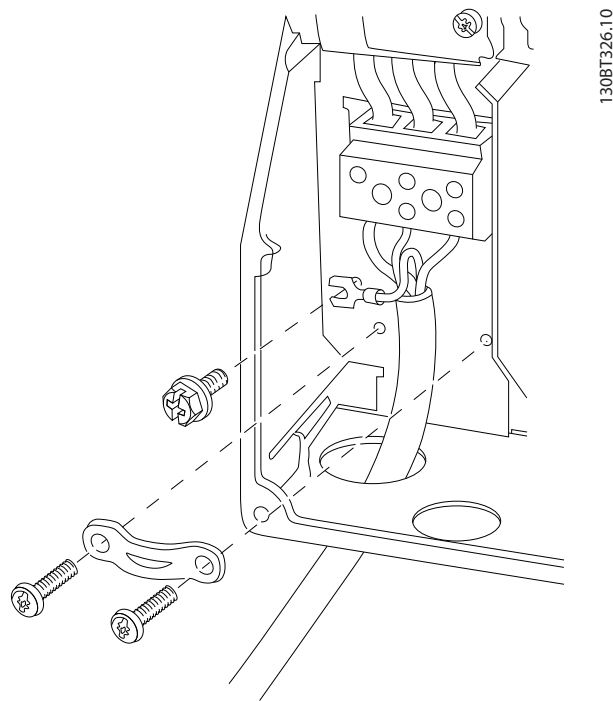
Подключение к сети для корпуса размера I6
